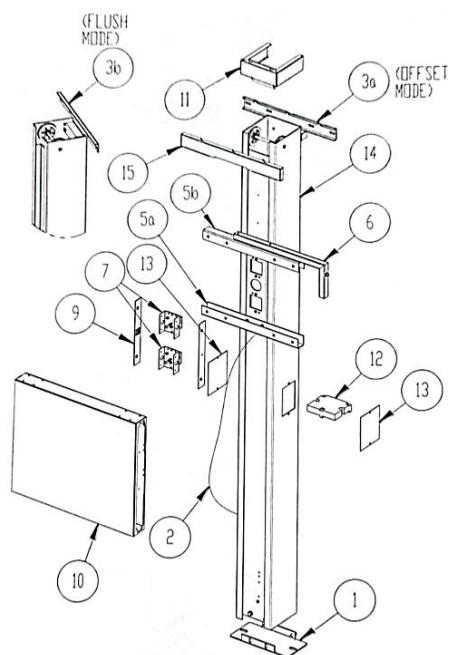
Partes del Bucky mural. Fuente tomado de (Summit Industries).
